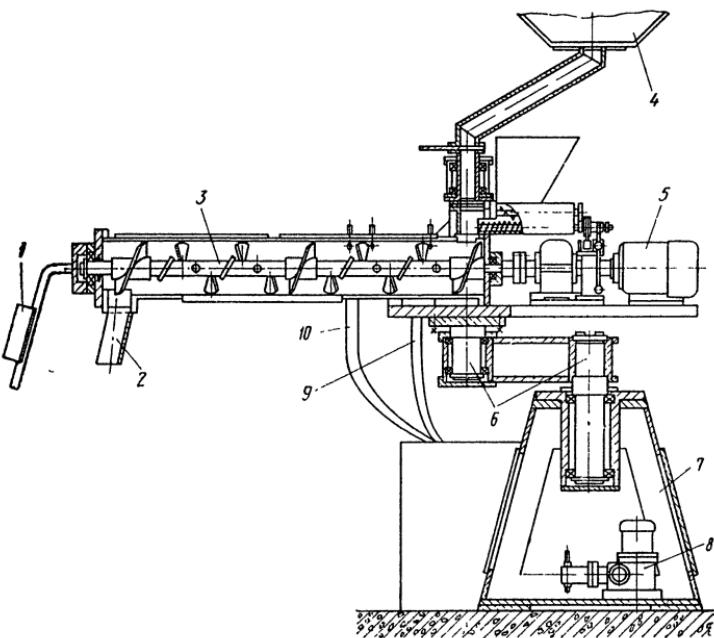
Полуавтоматическая поворотная установка для приготовления холоднотвердеющих смесей:
